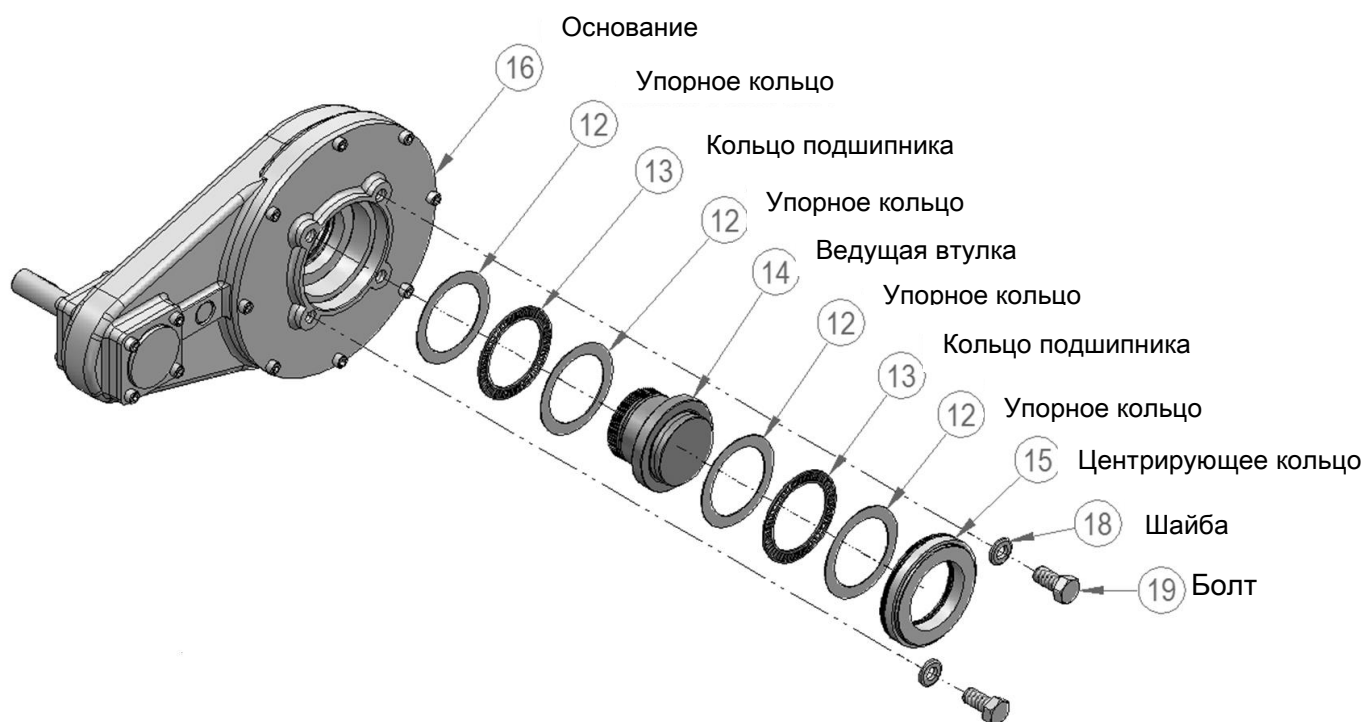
Ведущая втулка конического и цилиндрического редуктора в сборе
